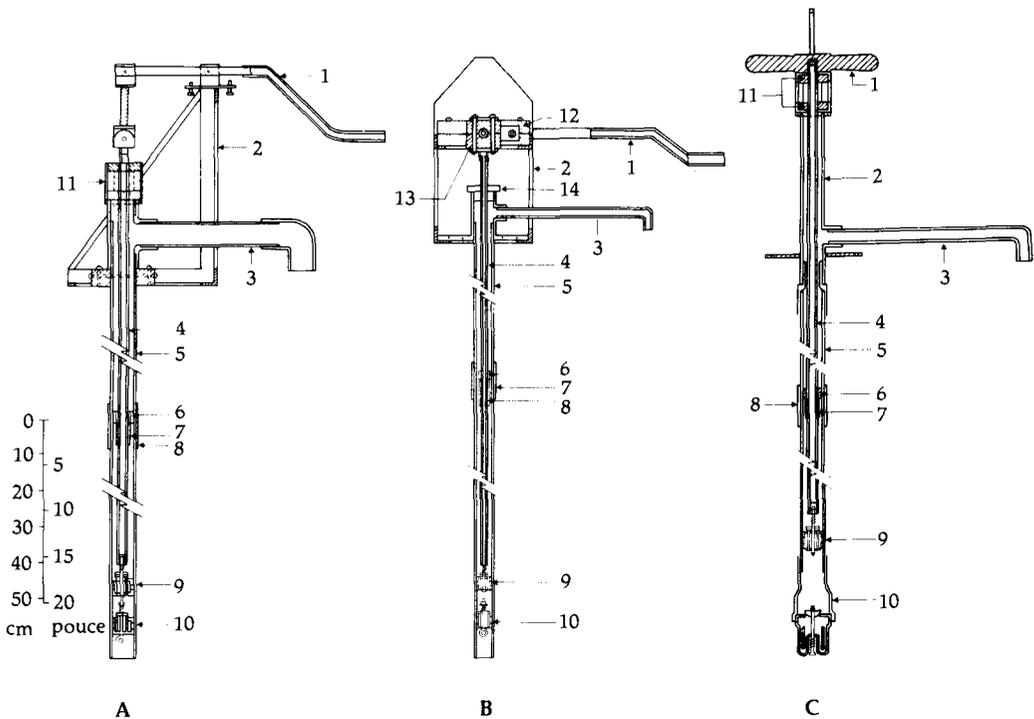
(A) Pompe L1, (B) pompe L3 et (C) pompe V1 : 1) bras ; 2) montant ; 3) dégorgeoir ; 4) tige du piston ; 5) colonne montante ; 6) guide de la tige de piston ; 7) raccord de la tige de piston ; 8) joint de la colonne montante ; 9) piston ; 10) clapet de retenue ; 11) coussinet et boîte de compteur en bois (L1 et V1) ; 12) coussinet principal (L3) ; 13) palier de tête de bielle (L3) ; et 14) contre-base (L3).
